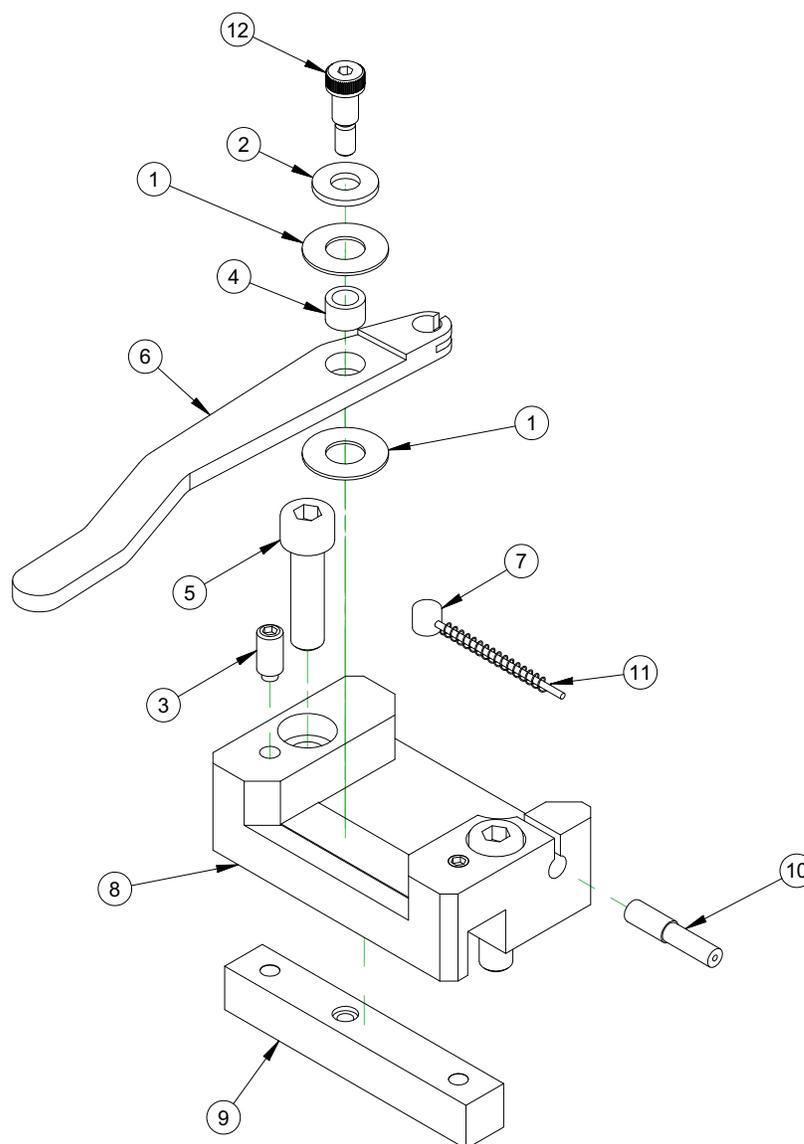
LISTE DES PIÈCES ENSEMBLE AXE RADIAL (P/N 86890)
